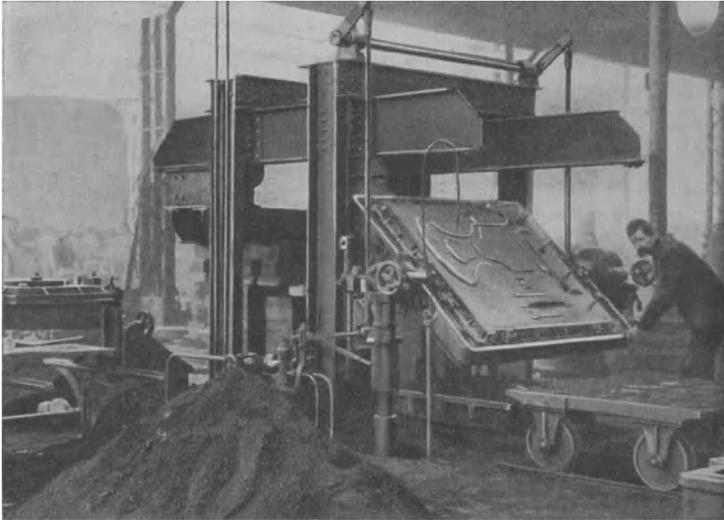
Große hydraulische Wendeplatten-Formmaschine (Hainholzer Schmirgelfabrik).
